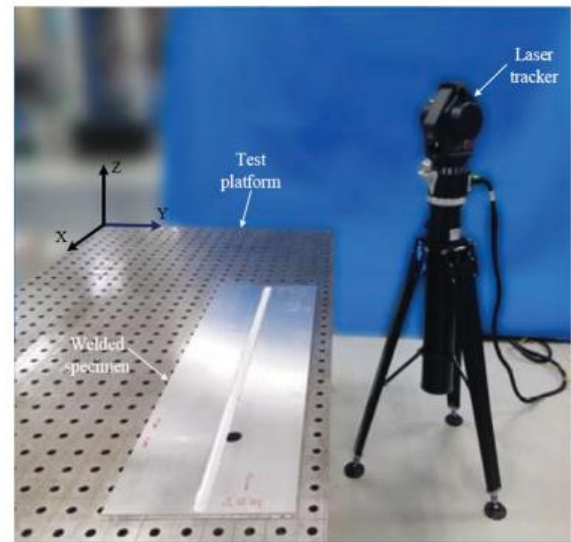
Зварювальний зразок та лазерно-вимірювальний пристрій [19].
